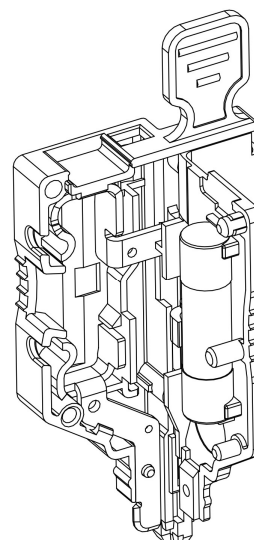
защитный предохранитель размером 5x20 мм, установленный в паз держателя
